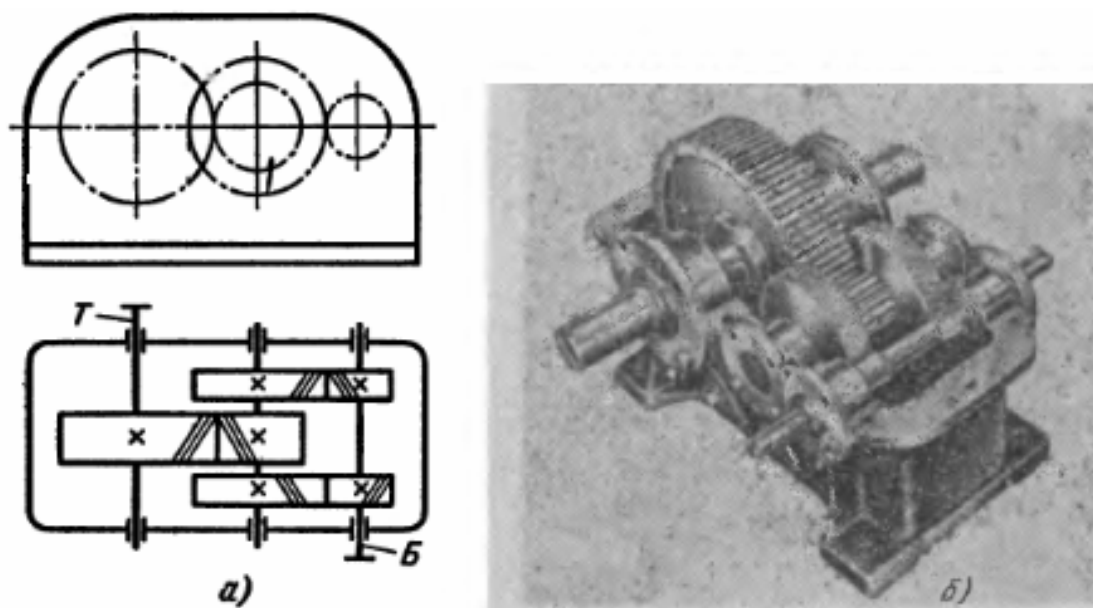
Цилиндрический двухступенчатый горизонтальный редуктор с раздвоенной быстроходной ступенью:
